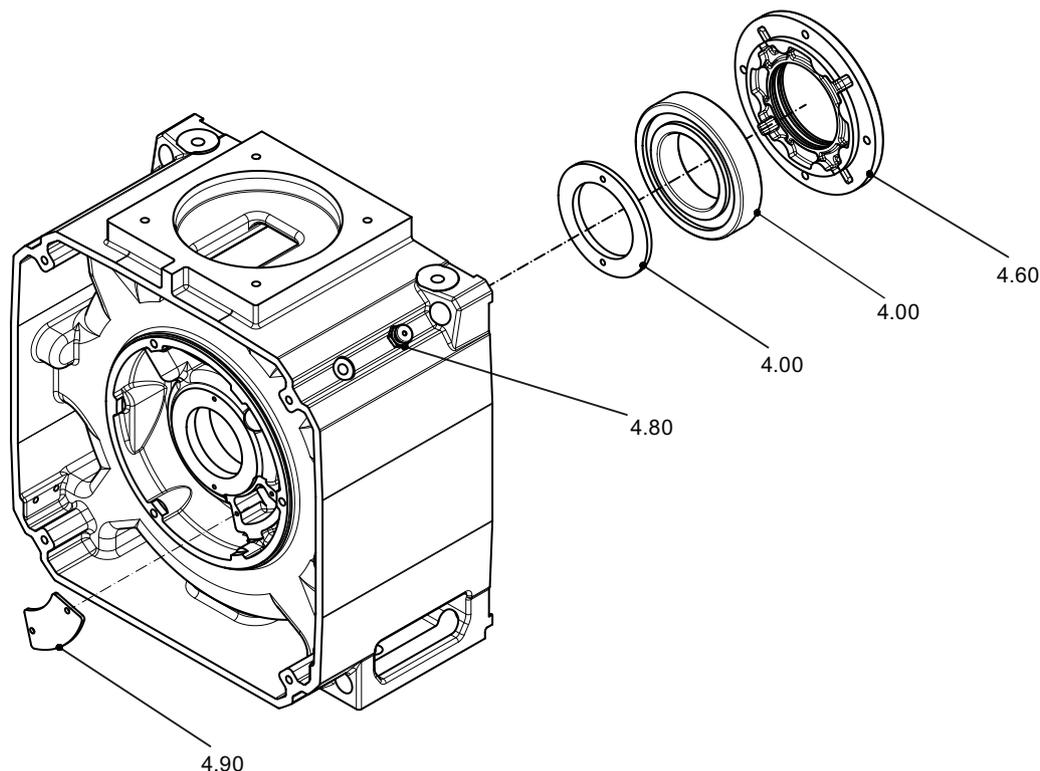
Запчасти Узел подшипника качения неприводная сторона, с дополнительной смазкой
